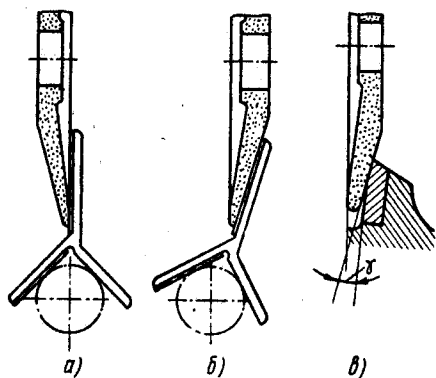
Установка шлифовального круга при заточке передней поверхности развертки:
